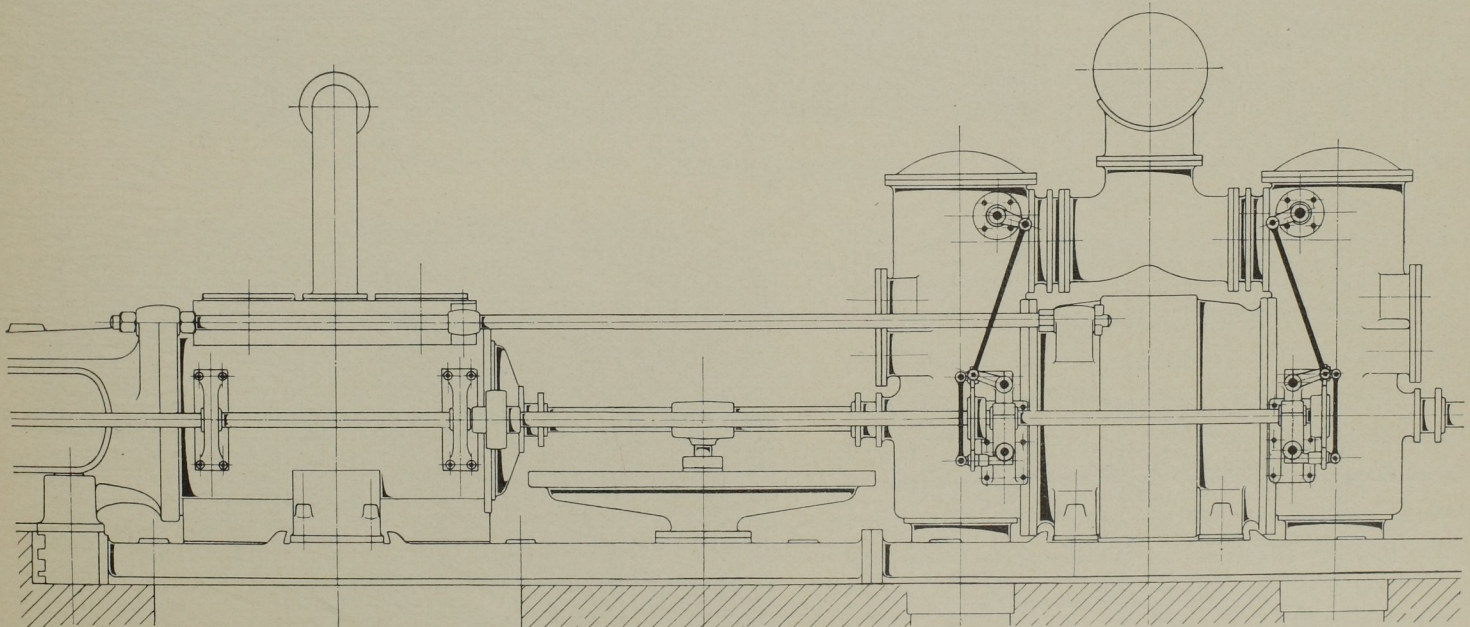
Seitenansicht der Gebläsemaschine. Massst. 1:50.
